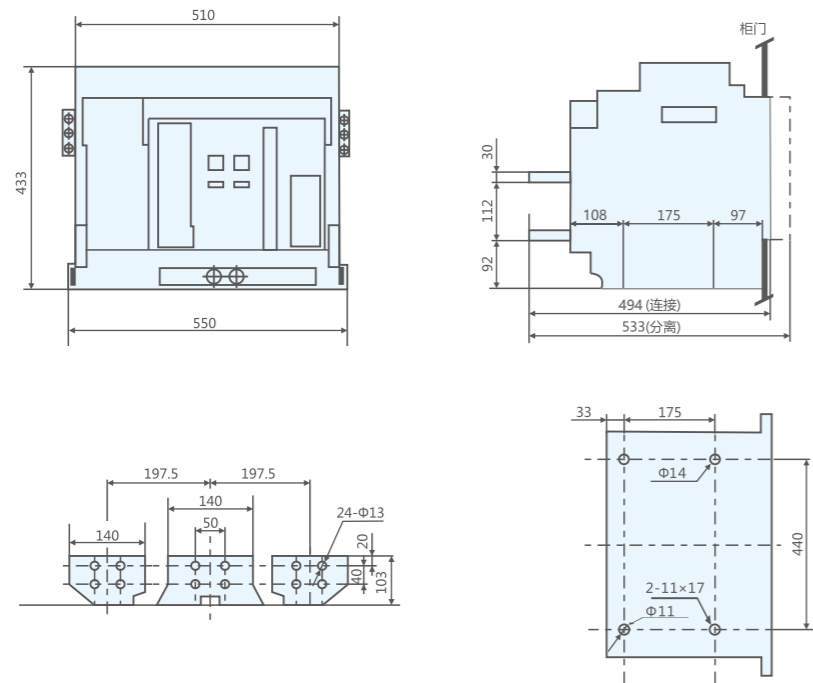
抽屉式断路器安装尺寸及外形尺寸 (FTW1-4000/3, In=3600A、4000A)
